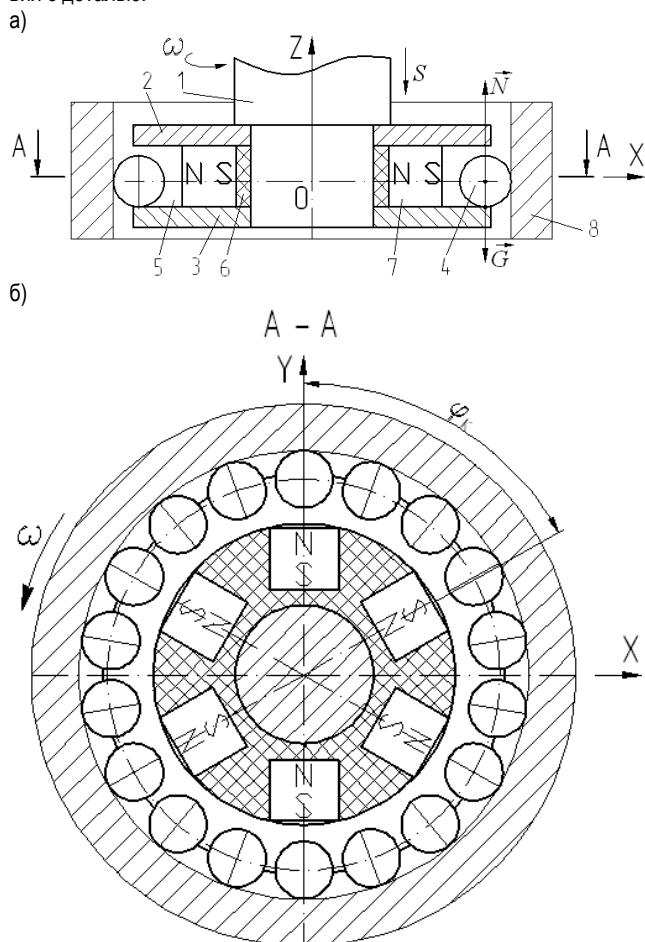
Схема магнитно-динамического упрочнения поверхности детали: а) общий вид схемы; б) поперечное сечение инструмента
